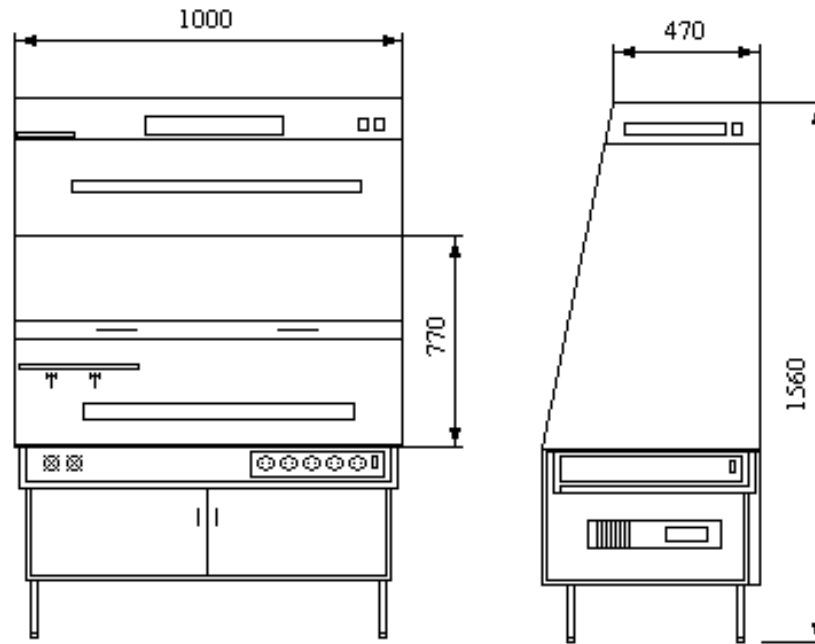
Витяжна шафа для виготовлення печатних плат
